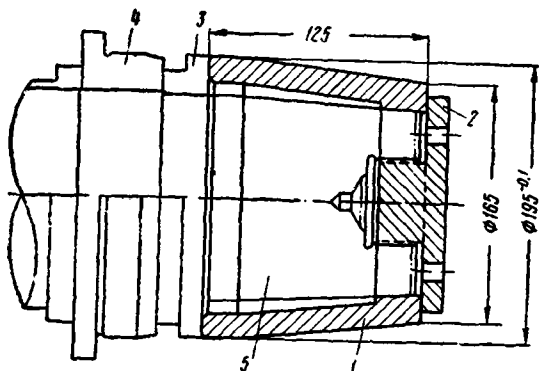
Монтаж оправки на конусе вала перед сборкой якоря с остовом двигателя НБ-406:
